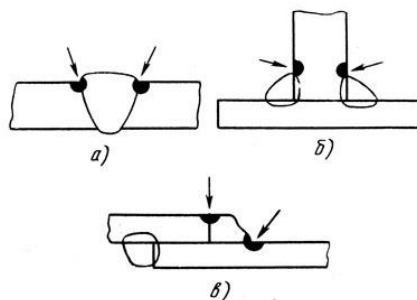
Подрезы зоны сплавления: а - стыкового, б - углового, в - нахлесточного
